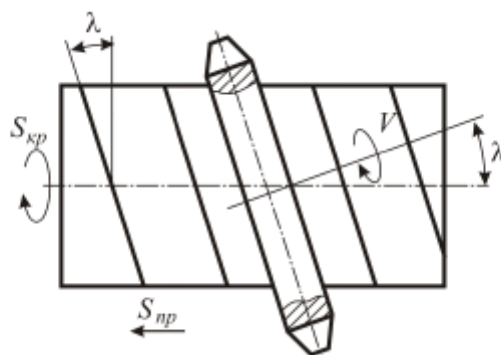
Схема нарезания червяка с помощью дисковой фрезы.
